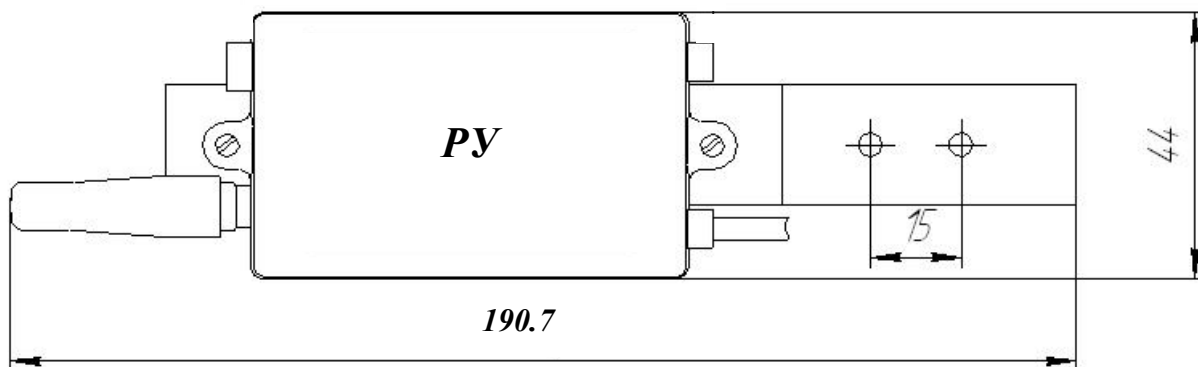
Габаритные и установочные размеры радиоудлинителя RS-232 (RS-485)
